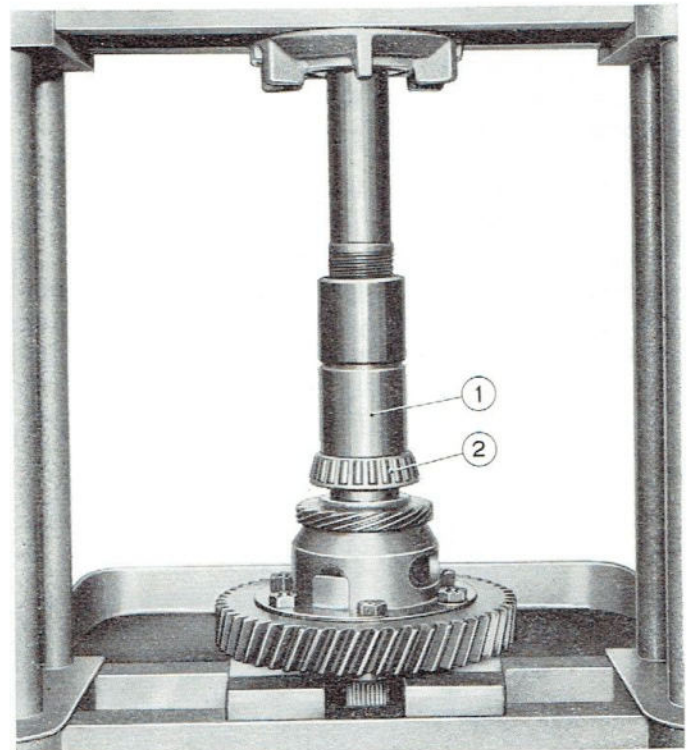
Einpressen des Ausgleichgehäuselagers.
